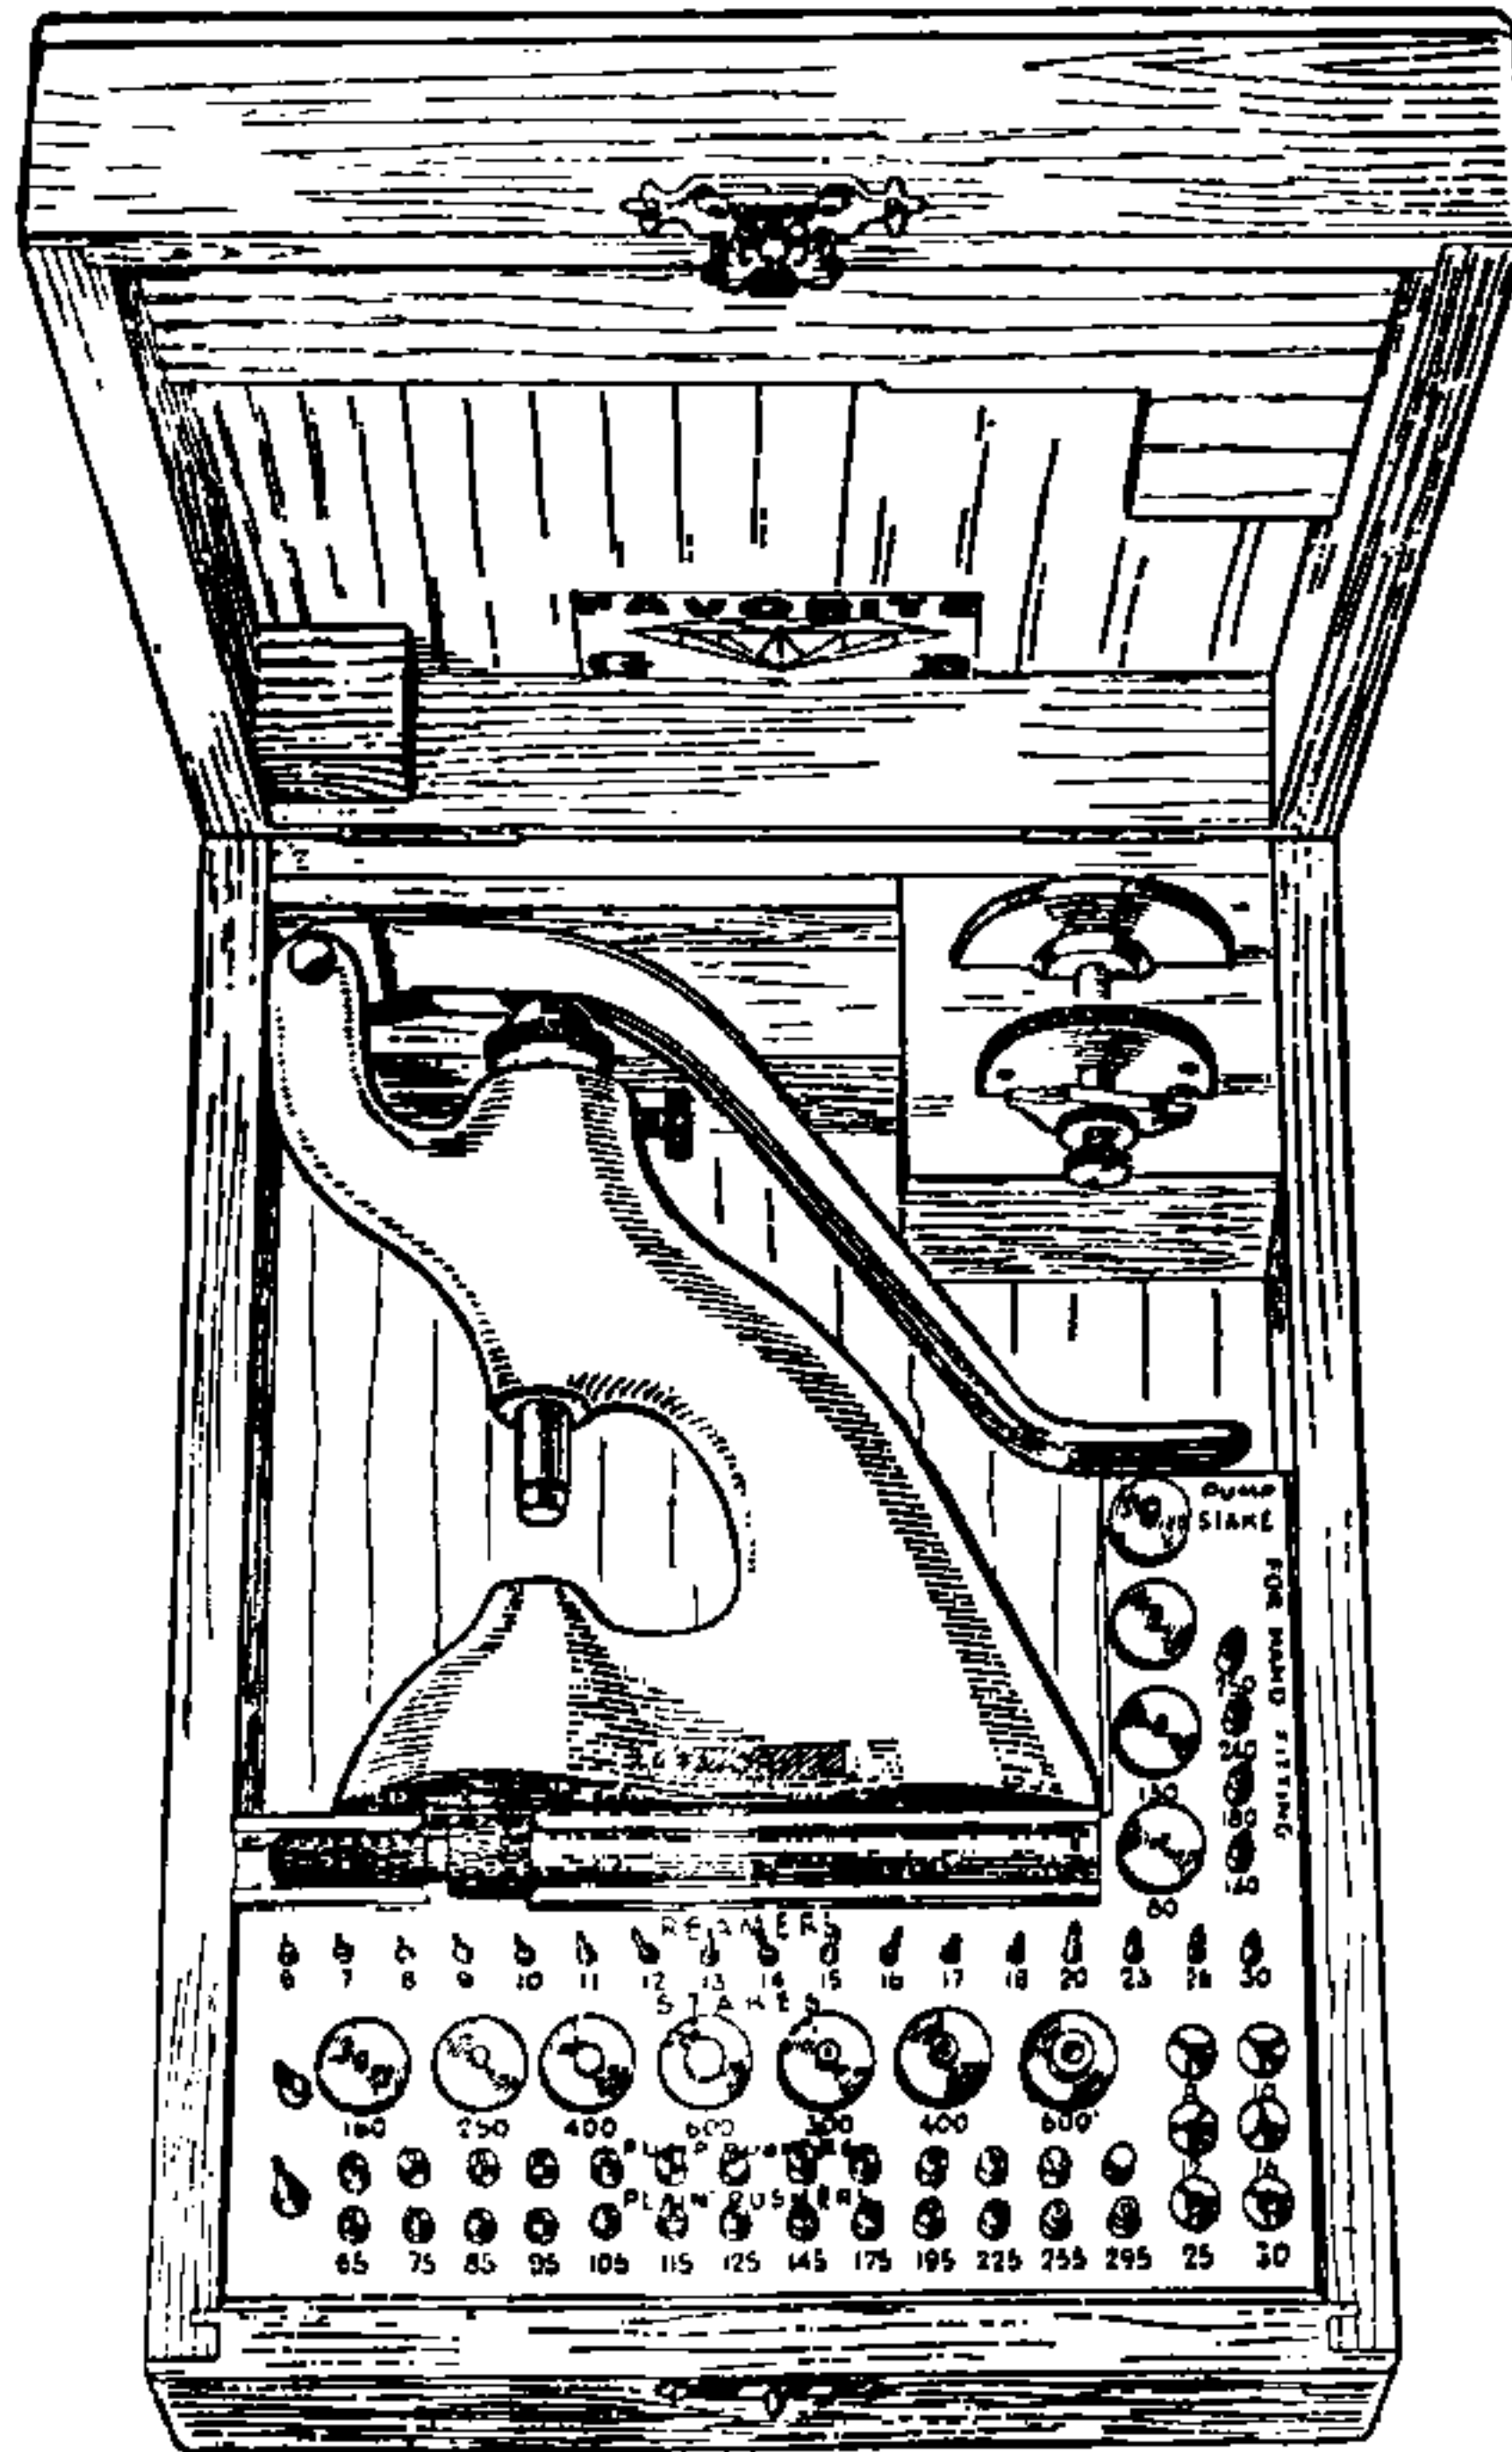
Equipaggiamento per collocare in posizione le pietre.
